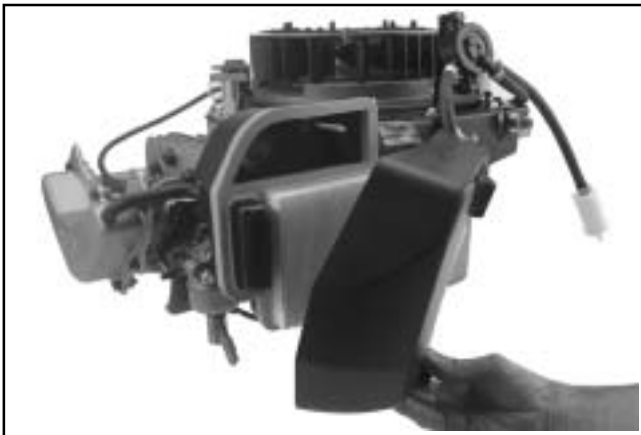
Desmontaje de la tapa del filtro de aire.
